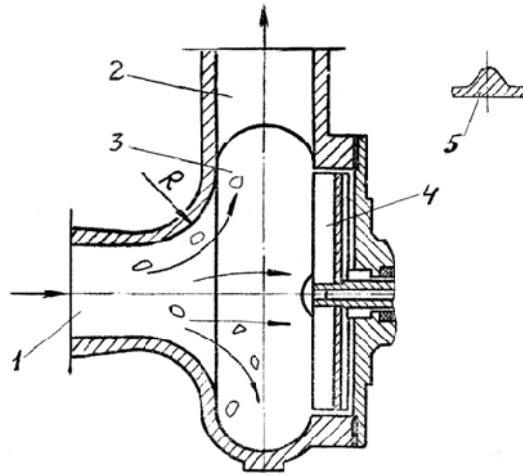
Свободновихревой насос со сглаженными лопастями рабочего колеса: 1 - вход; 2 - выход; 3 - свободная камера; 4 - рабочее колесо; 5 - профиль лопасти рабочего колеса
